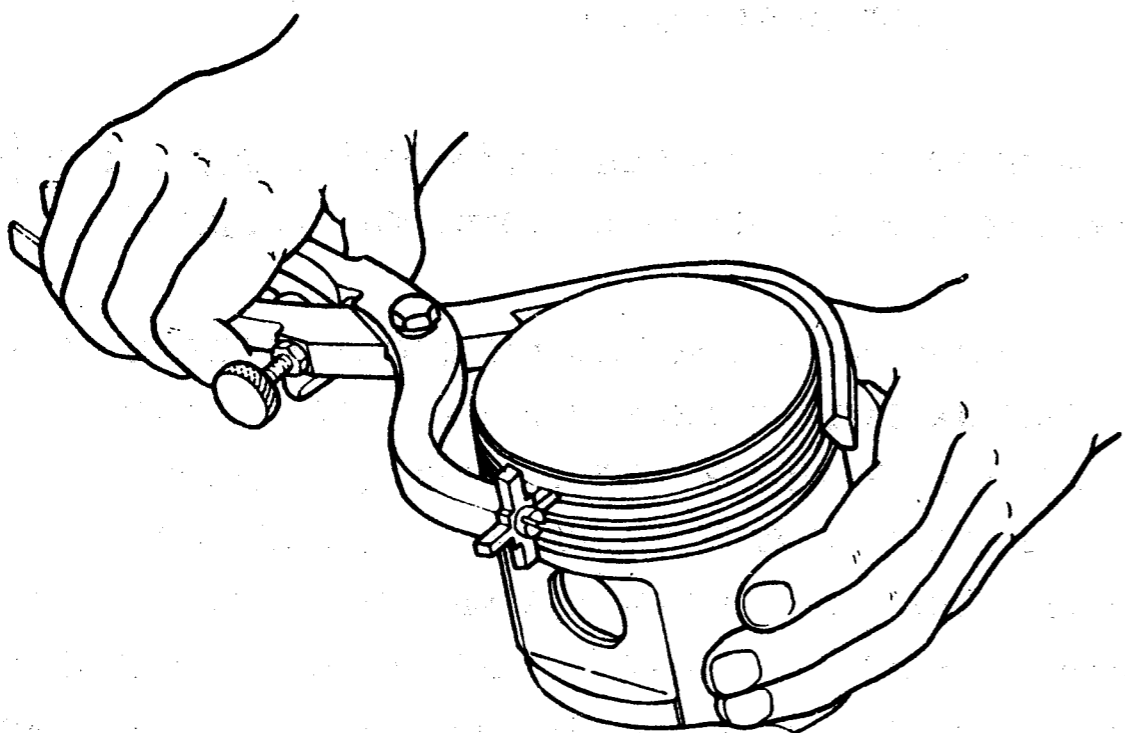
Очистка нагара в канавках поршней с помощью приспособления 5-У-2769I
